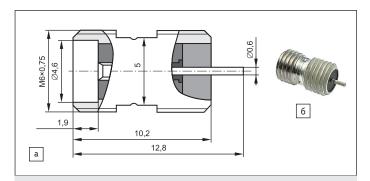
Соединитель СРГ50-751ФВ: а) конструкция; б) внешний вид
